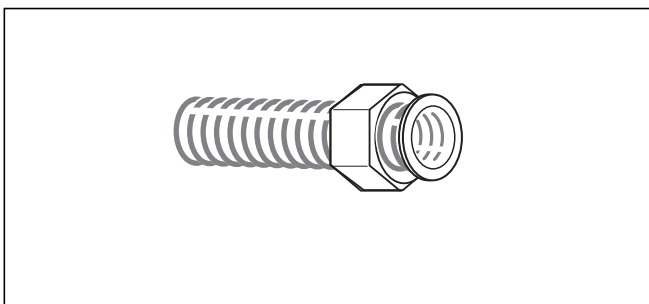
Doppelnippel ausschrauben. Vorstehende Welle muss komplett zusammengestaucht sein.
